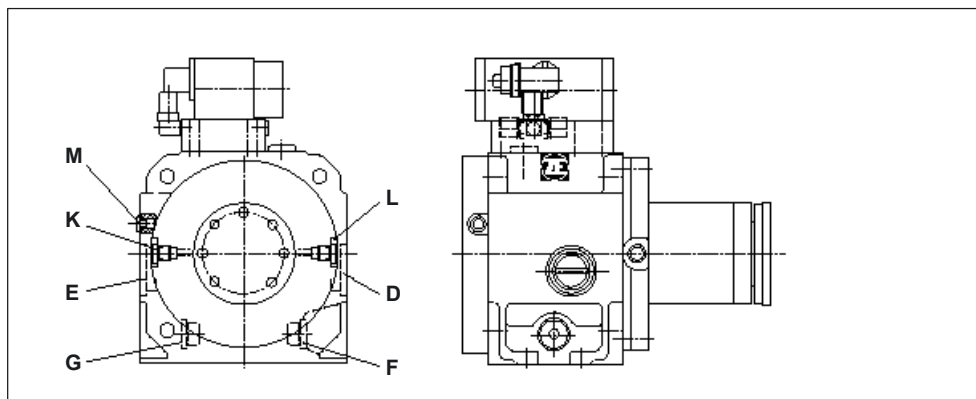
Переключаемый редуктор с блоком переключения для типоразмера 100
